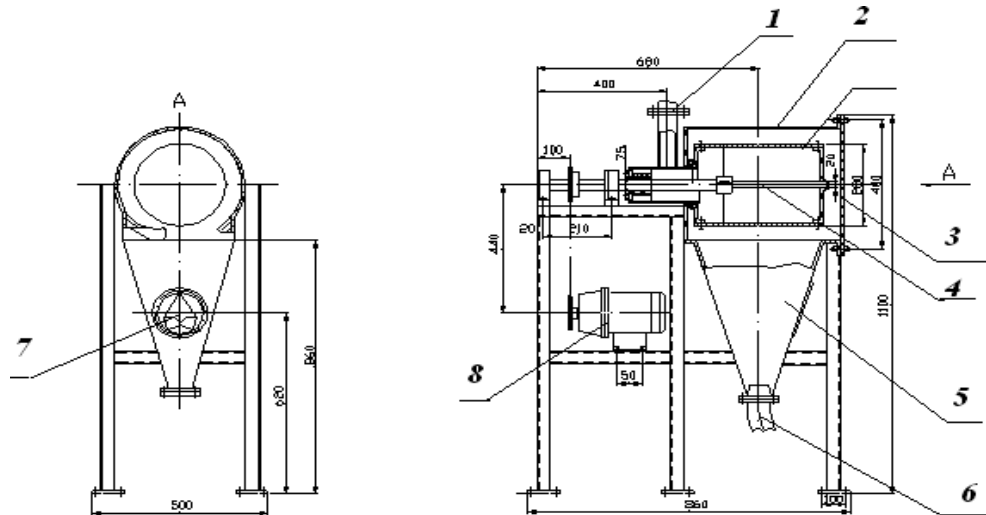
Пневмопросіювач: 1 патрубок подавання борошна; 2 – корпус; 3 – кришка; 4 – вал ; 5 – патрубок для просіяного борошна; 6 – трубопровід; 7 – магнітні уловлювачі; 8 – циліндричне сито.
